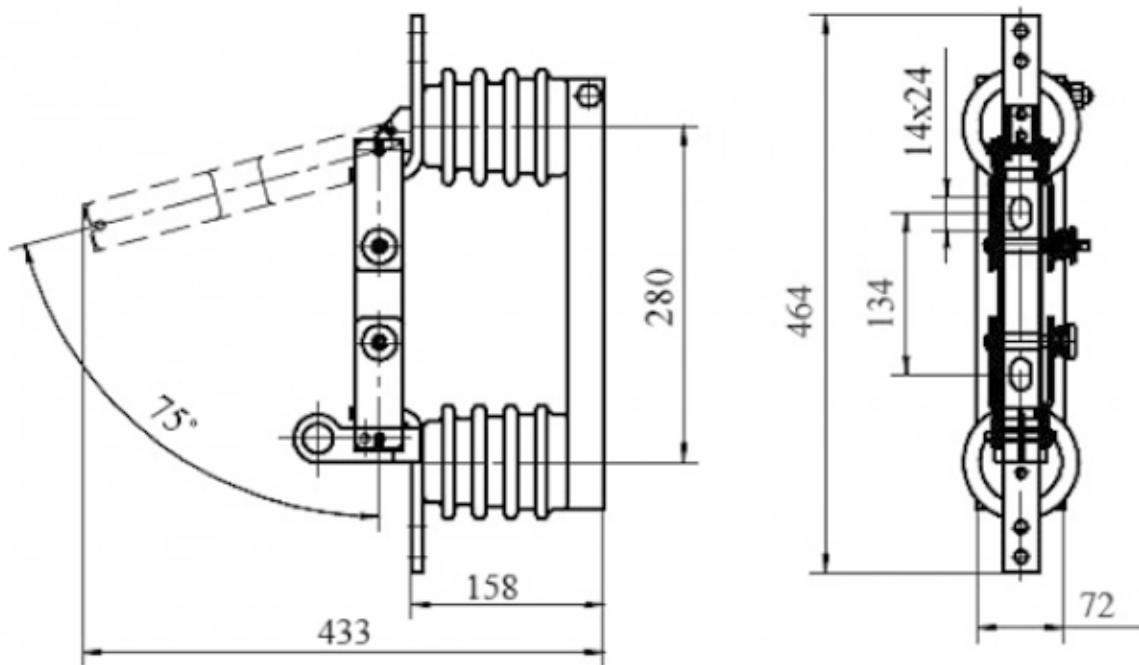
Разъединитель внутренней установки типа РВ3, заземляющие ножи с двух сторон
